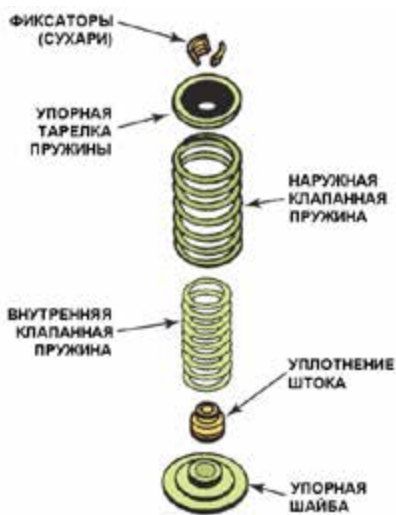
Типичный тарельчатый клапан и связанные с ним компоненты. Двойные клапанные пружины используются для уменьшения вибрации клапанного механизма, а упорная шайба пружины используется для защиты алюминиевой головки от повреждения; источник: Pearson Education, Inc.
